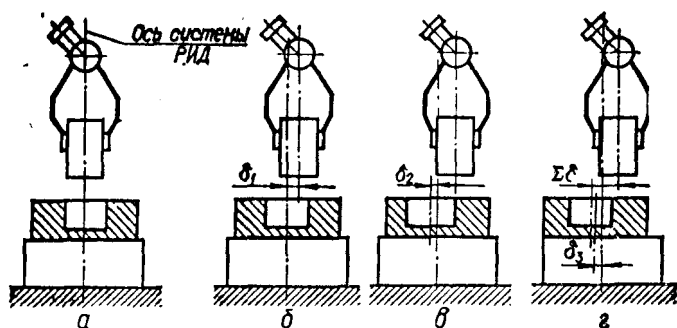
Ошибки позиционирования: а – идеальный случай; б – ошибка позиционирования робота; в – ошибка изготовления детали; г – ошибка установки детали.
